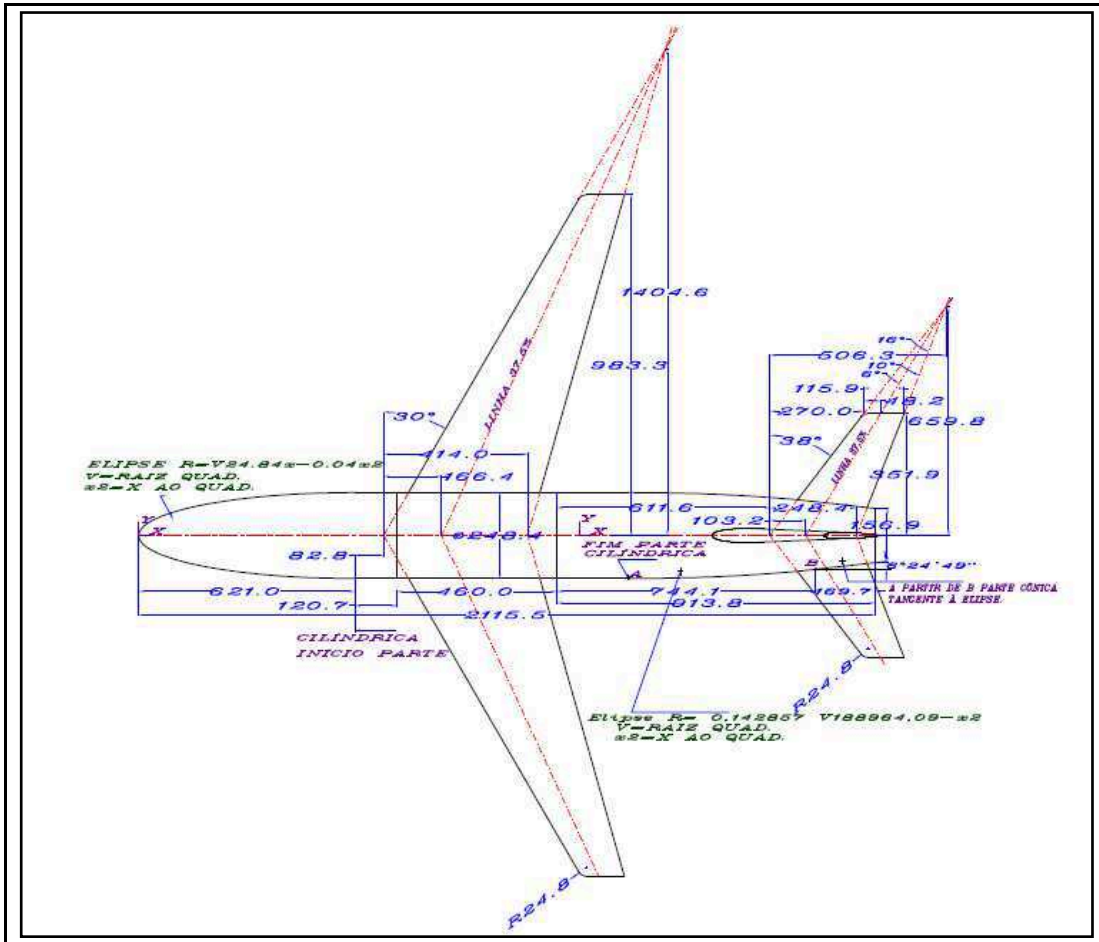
Vista em planta do modelo M5-2xPlus (CANHOTO, 2009)
